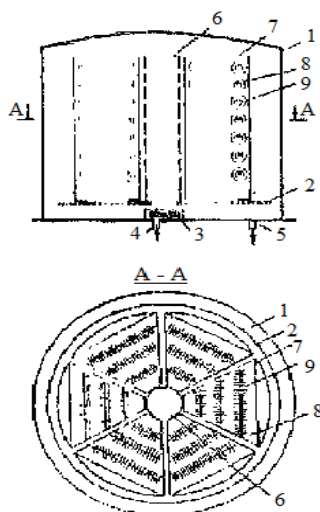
Устройство для термообработки листов магнитопроводов: вертикальный и горизонтальный в сечении А - А разрезы
